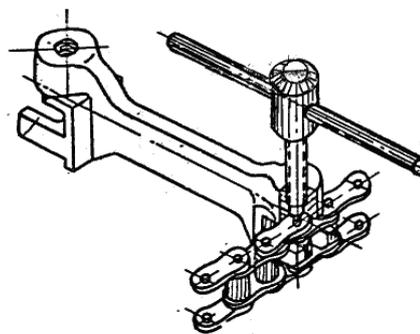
Приспособление для разборки втулочно-роликовых цепей
